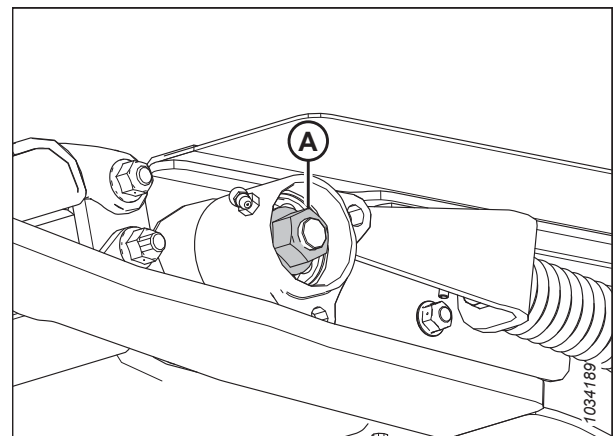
Rodamiento de rodillo tensor: lado izquierdo
